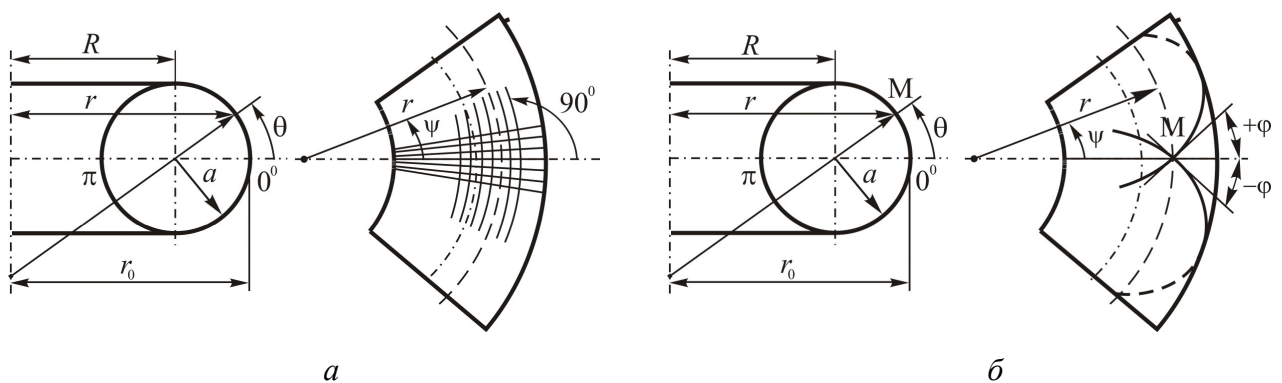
Схема продольно-поперечной (а) и спиральной (б) намотки круговой тороидальной оболочки
